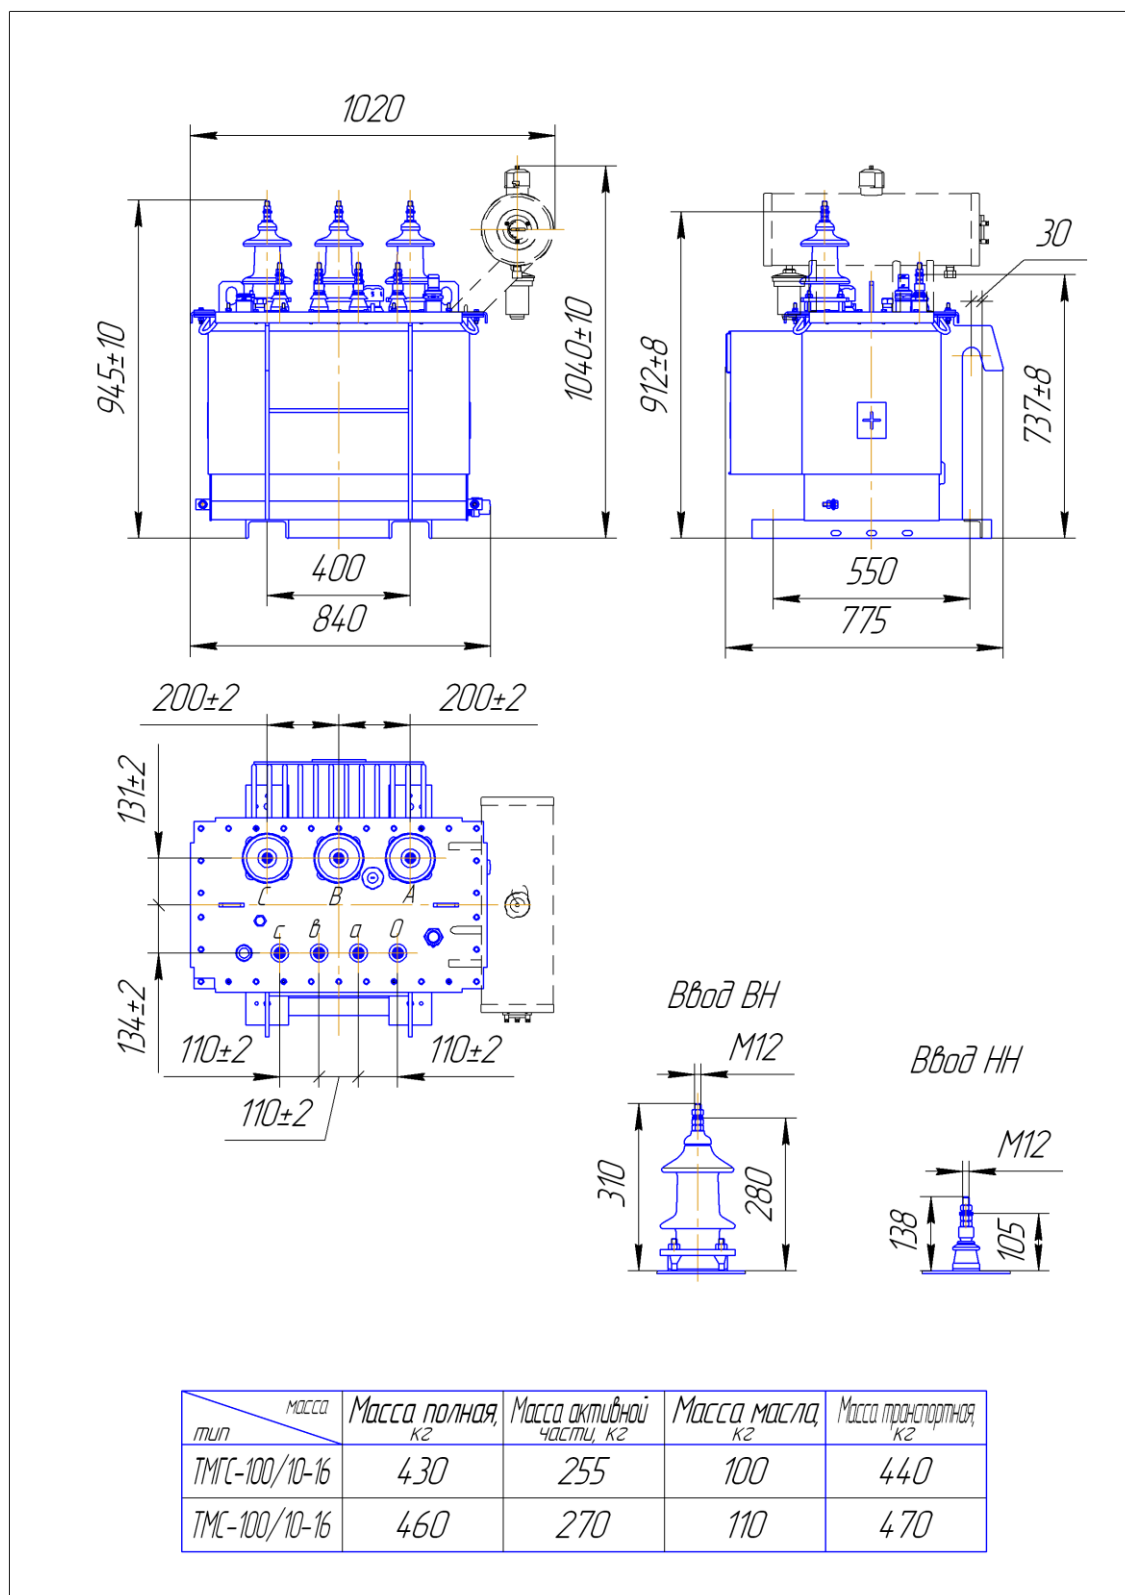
Габаритные, установочные и присоединительные размеры трансформатора ТМГС - 100/10-16
